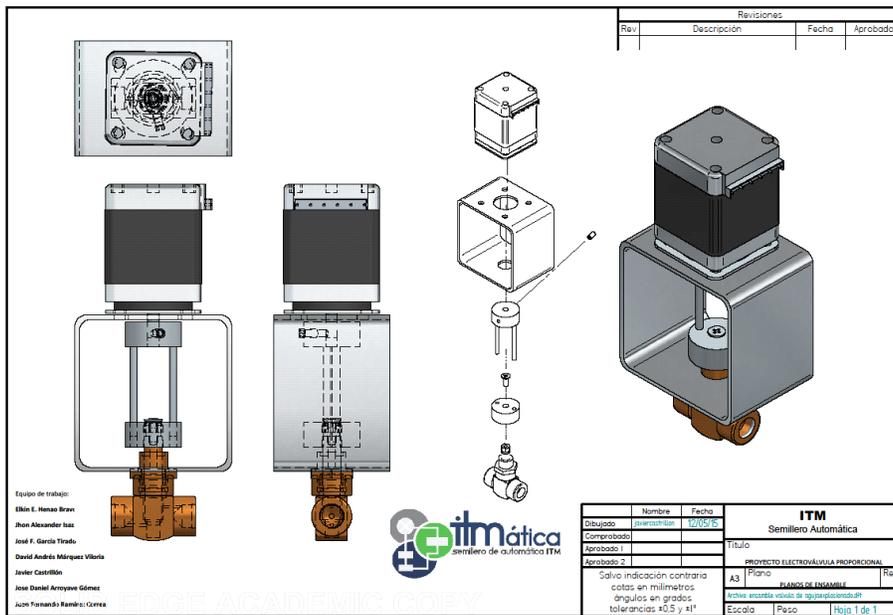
Plano de la electroválvula tipo aguja explosionada, detallando cada una de sus piezas.
